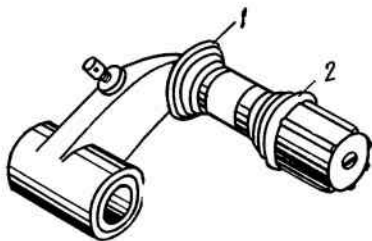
Общий вид каретки придерживающих роликов транспортирующих зубчатых барабанов
